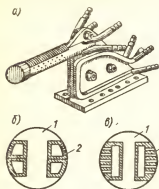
Петлевой индуктор с магнитопроводом для закалки внутренних поверхностей способом одновременного нагрева при вращении закалываемой детали: а — общий вид индуктора, б — конструкция с отдельными камерами для охлаждения индуктора и для выхода закалочной воды; в — конструкция без постоянного охлаждения:
